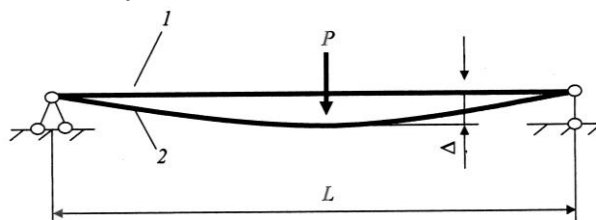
Схема взаимодействия двух верхних листов в процессе прессования: 1 – первый верхний лист пакета, соприкасающийся с верхней плоской плитой пресса; 2 – второй лист
